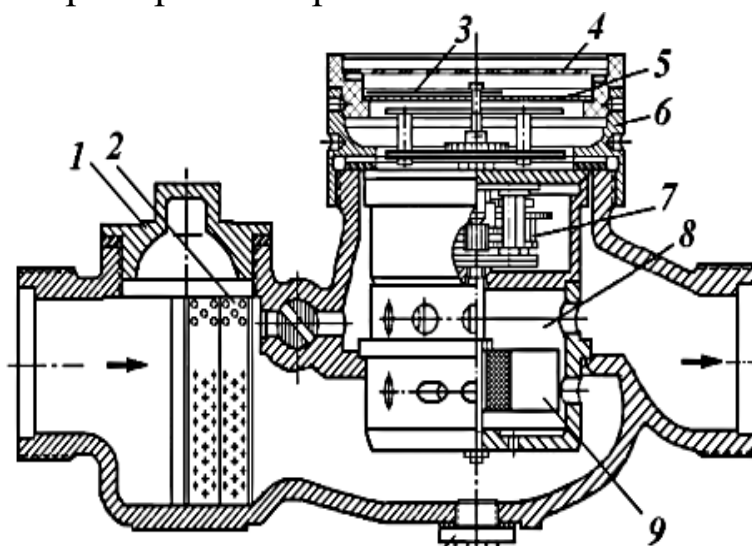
Дозатор воды турбинного типа: 1 – корпус; 2 – сетка; 3 – стрелка; 4 – стекло; 5 – циферблат; 6 – поворотное кольцо; 7 – редуктор; 8 – камера крыльчатки; 9 – крыльчатка; 10 – пробка
